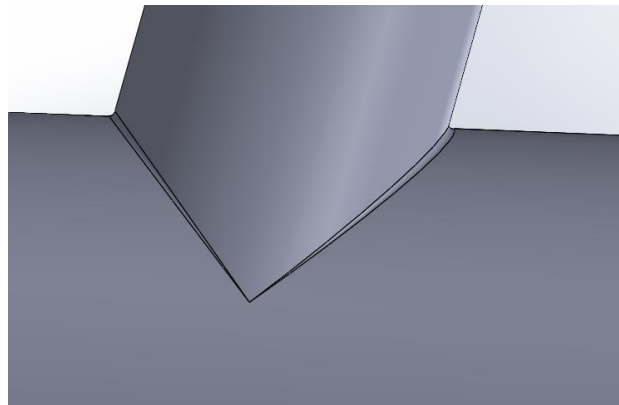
Tubo con reborde de soldadura (Fuente: Propia)
